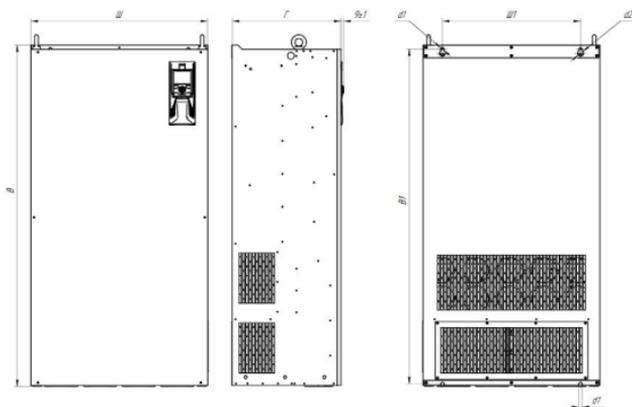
Габаритные и установочные размеры устройств серии INPRIME MX в металлическом корпусе (настенное исполнение), типоразмеры 5-13
